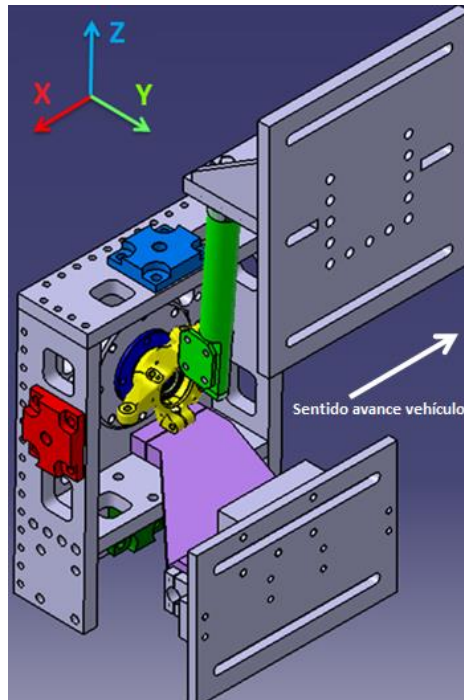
Montaje mediante utillajes de la disposición de la mangueta en el banco de ensayos
